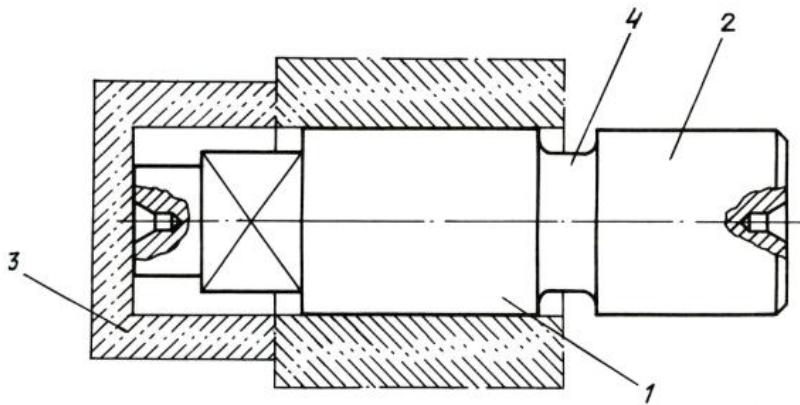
Схема придания заготовке фиксированного по длине оправки положения:
